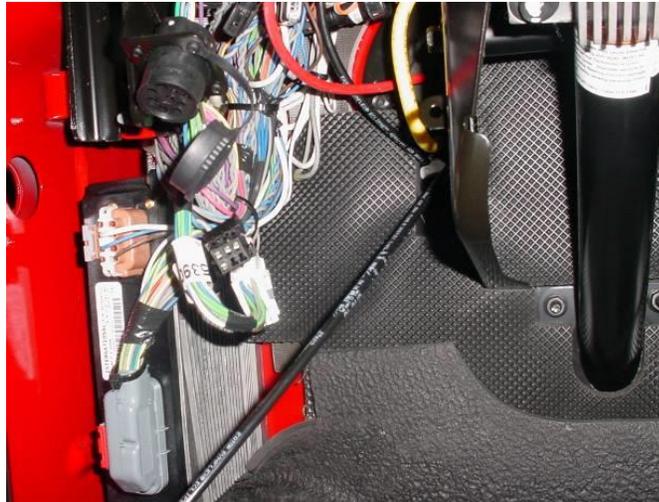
Pared de fuego, zona pedales sin remover tornillos de sujeción.
